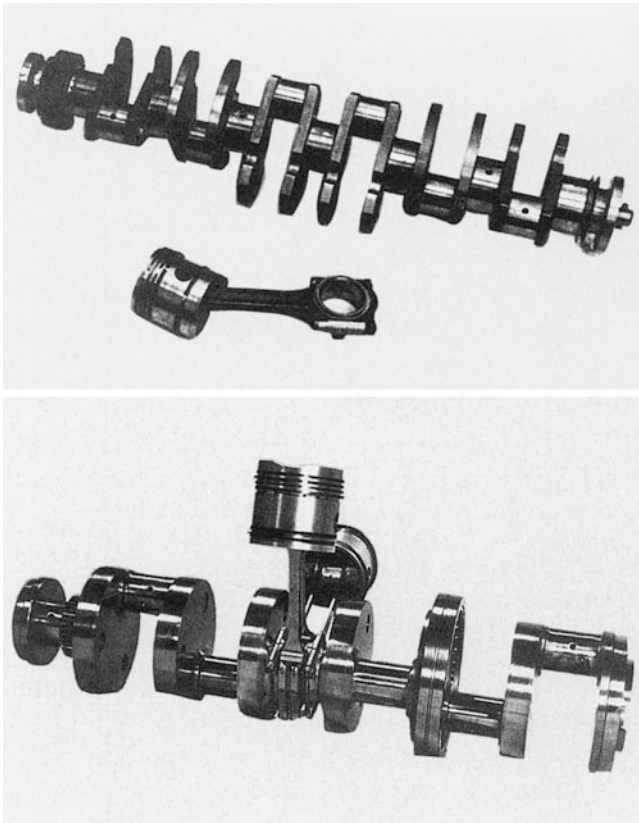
Gleitgelagerte Wangenkurbelwelle mit angeschmiedeten Gegengewichten des sechszyindrigen HL-62-Motors (Bohrung 105 mm, Zylinderabstand 132 mm) und rollengelagerte Scheibenkurbelwelle des Zwölfzylinder-V-Motors HL 230 (Bohrung 130 mm, Zylinderabstand 142 mm). Die Vorteile der Scheibenkurbelwelle für die Motorabmessungen sieht man an dem Verhältnis von Zylinderabstand zu Bohrung. HL 62: $z a/d = 1,26$; HL 230: $z Jd = 1,09$!
